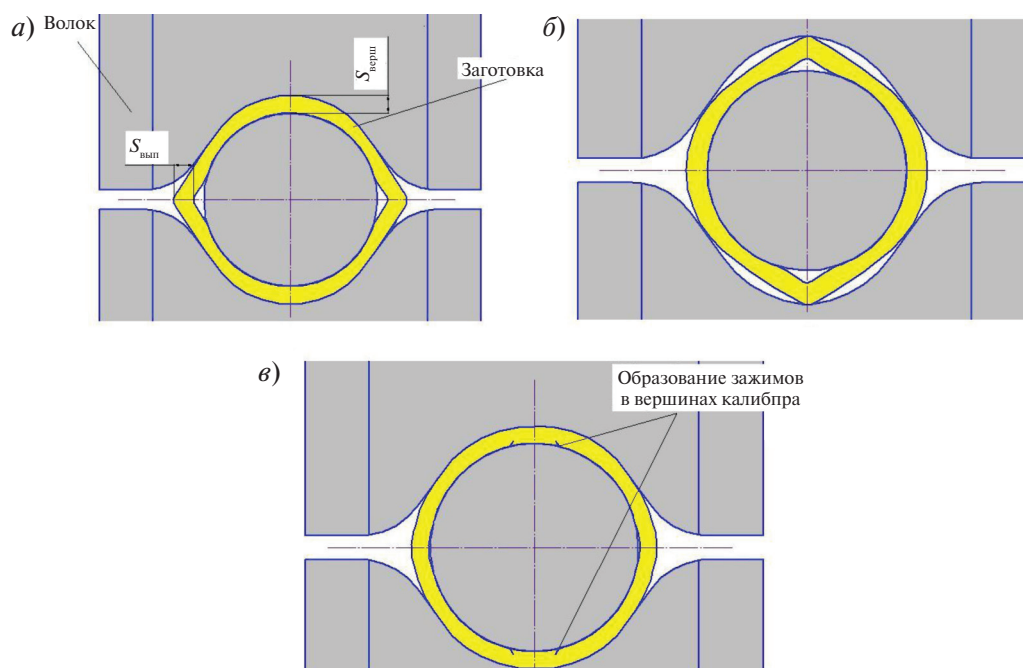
Схема образования дефекта «риска» на внутренней поверхности труб: а) формирование лампасов в выпусках калибра при прокатке в СПП-1; б) захват в вершинах калибра СПП-2 после кантовки трубы; в) формирование зажимов при заполнении металлом калибра
